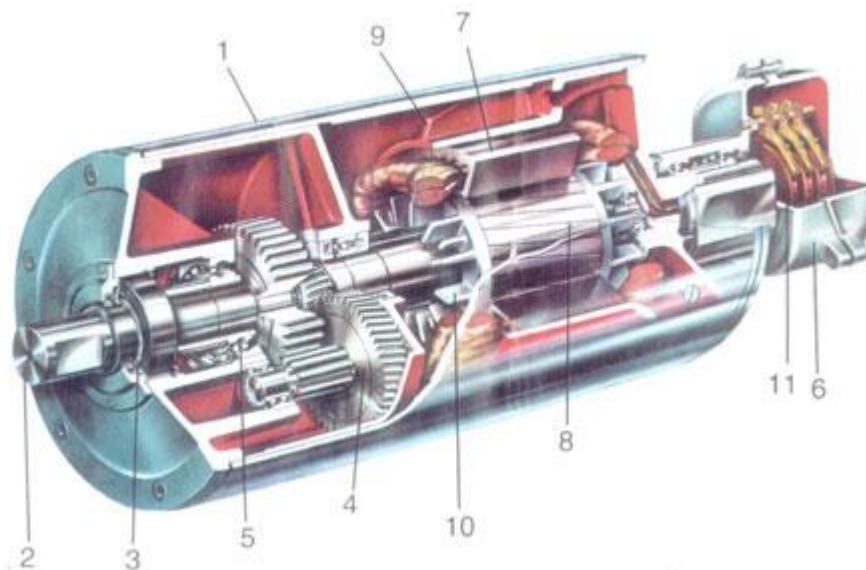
Мотор-барабан производства фирмы "Bauer" (ФРГ): 1 - барабан; 2 - монтажная шейка вала; 3 - уплотнение; 4 - зубчатые колеса; 5 - подшипники; 6 - клеммная коробка; 7 - статор; 8 - ротор; 9 - ребра для отвода тепла; 10 - крылья ротора; 11 - блок с контактными кольцами
